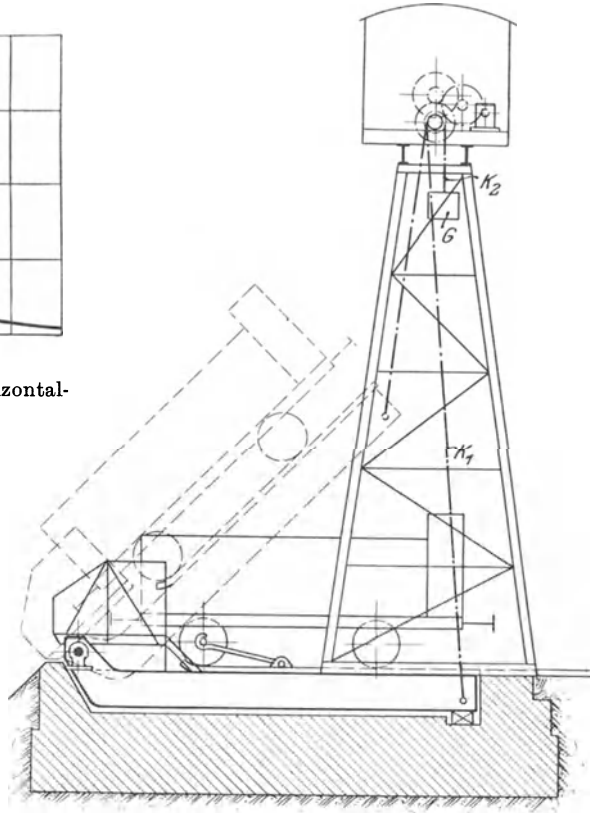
Niveauekipper mit Windengerüst nach Gebauer.
